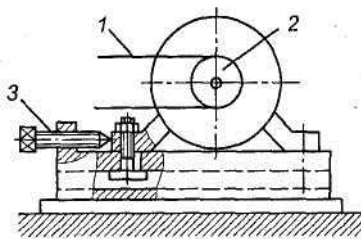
Регулировка натяжения ремня перемещением двигателя: 1 — ремень; 2 — шкив; 3 — натяжное устройство
